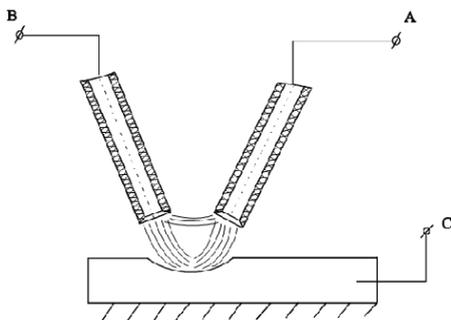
Схема сварки трехфазной дугой плавящимися электродами
